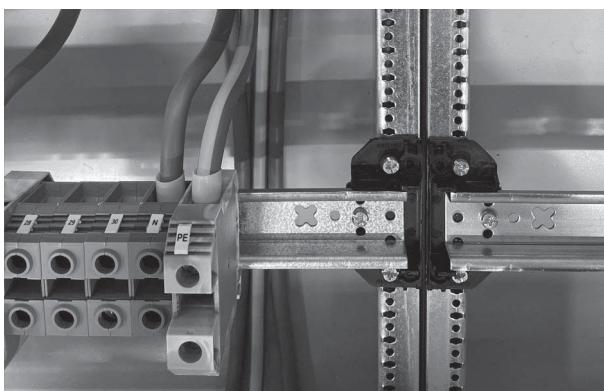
Beispiele isoliert aufgebauter Reihenklemmentragschienen mit PE-Reihenklemme
